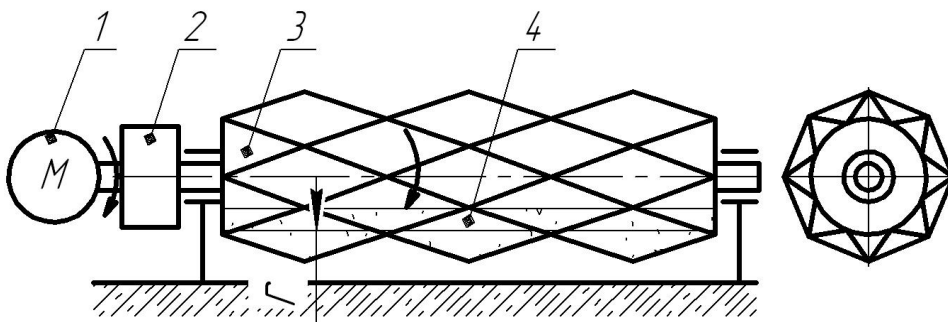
Схема барабанної мішалки і з нахиленими під різними кутами робочими поверхнями
